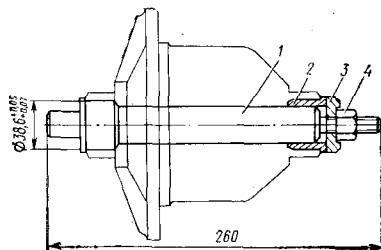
Центровая оправка для шлифования накатанной шейки коробки сателлитов:
